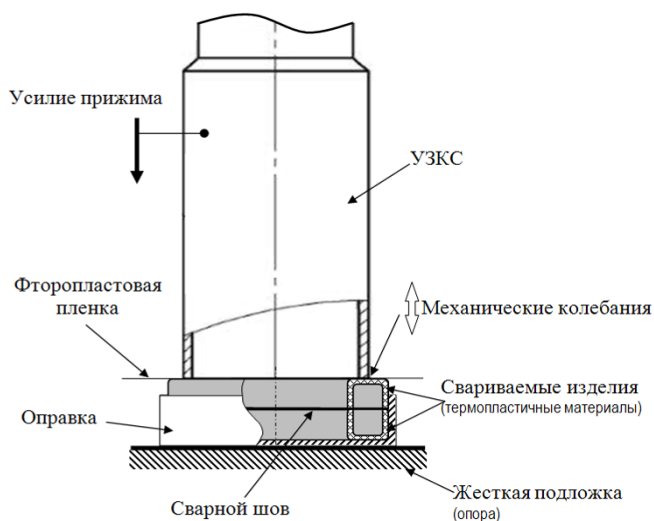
Схема процесса УЗ сварки деталей.
